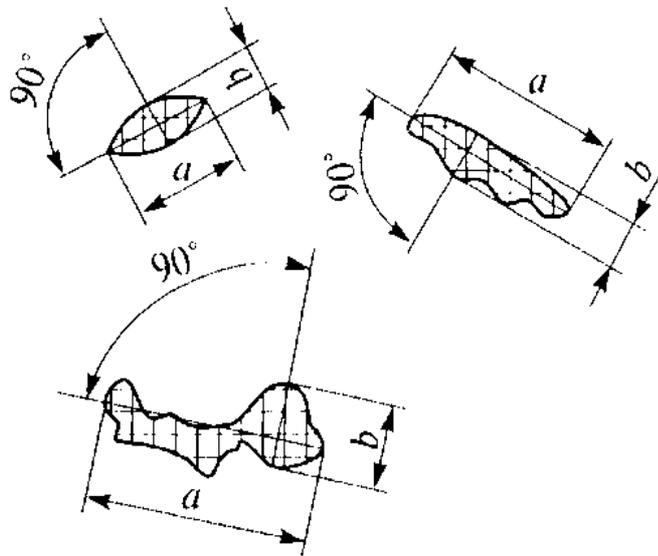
Максимальные размер и ширина постороннего включения в сварной шов
